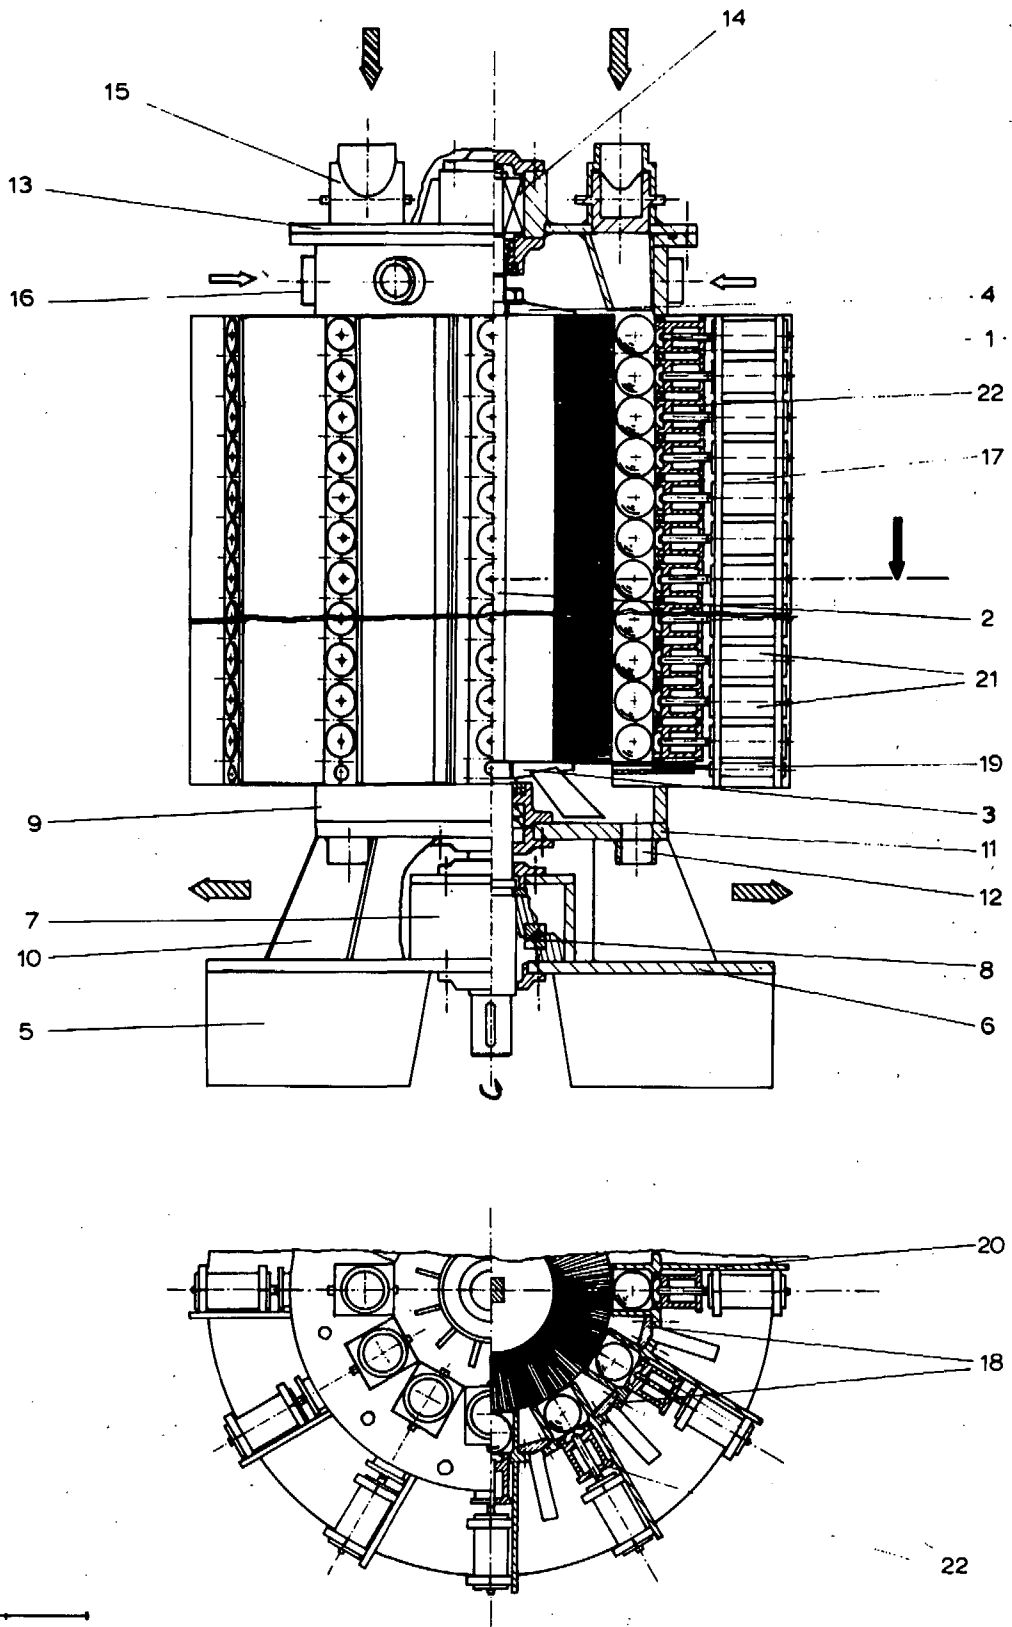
Prinzipskizze einer Kugelaufbürstmaschine (Techniktyp) - Erläuterung im Text -
